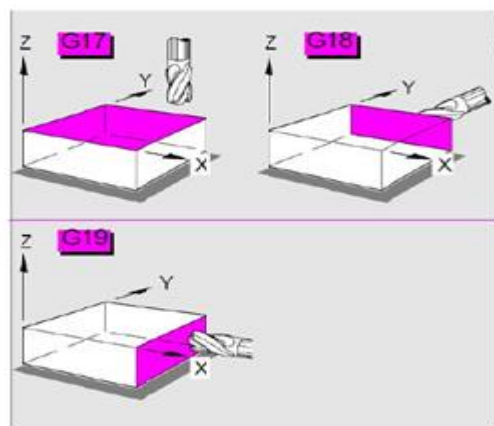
Choix du plan d'usinage en fraisage [3].
